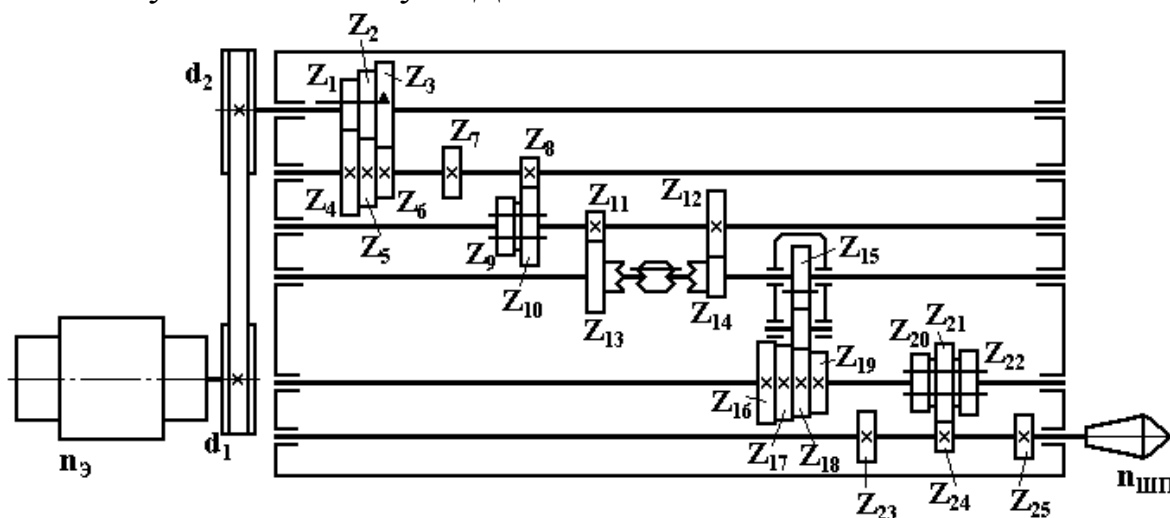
Кинематическая цепь главного движения условного станка (вариант № 1)
